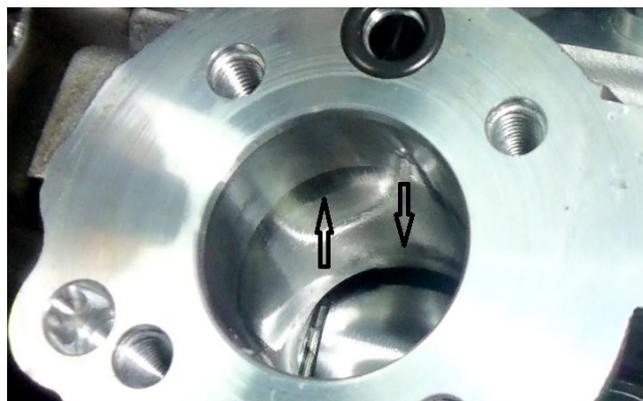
Следы изнашивания в отверстии под толкатель плунжера корпуса ТНВД
